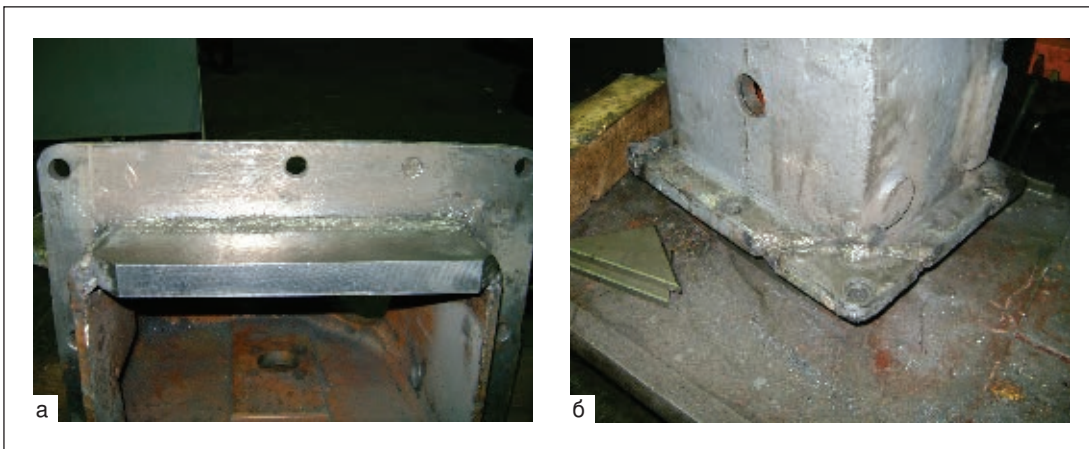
Общий вид восстановленного корпуса редуктора малого привода эскалатора: а — вваренная стальная стенка; б — углы фланца
